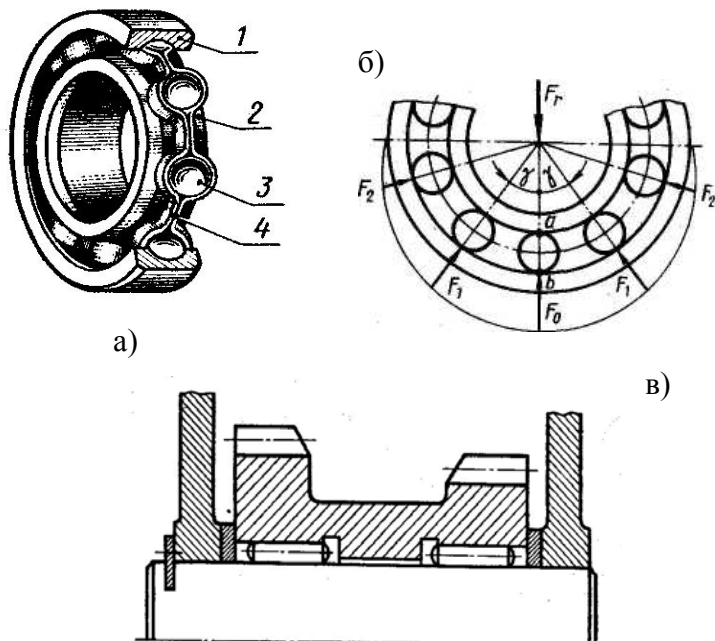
Подшипники качения: а) шариковый радиальный подшипник; б) схема распределения нагрузки между телами качения в подшипнике; в) блок зубчатых колес на подшипниках с игольчатыми роликами
